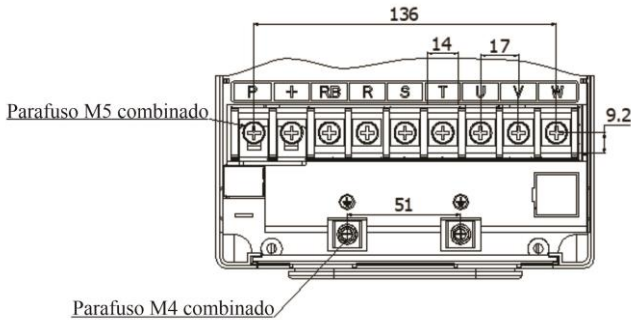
Terminal circuito principal 15~22kW G3 (Chassis No.: A4)
